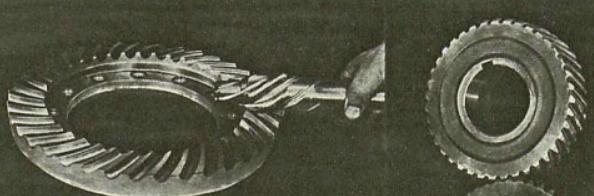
Так выглядят шестерни с новым зацеплением в главной передаче автомобиля ГАЗ-63.
